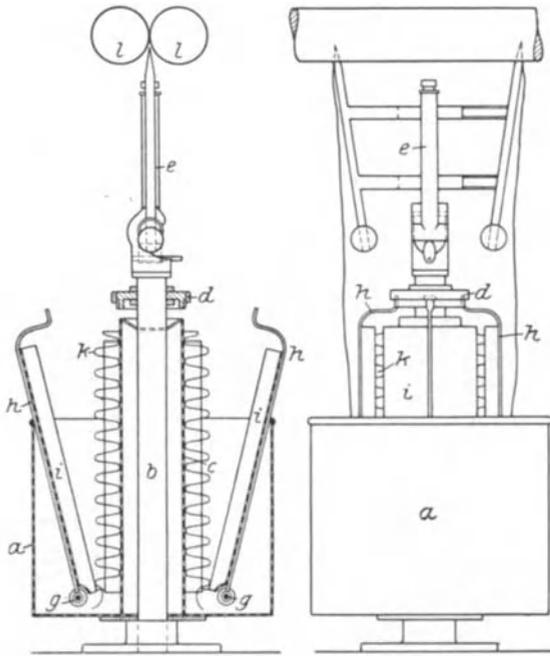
Umkehr- und Rollmaschine D.R.P. 230313; Maschinenfabrik Arbach G. m. b. H., Reutlingen i. W.
